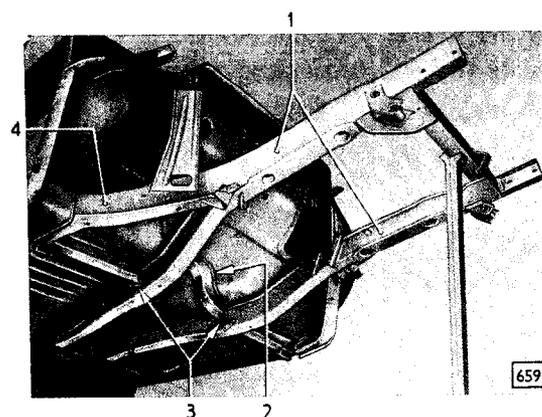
Vorderrahmen bei vollständig abgetrennten Seitenstreben in Einbaulage bringen
